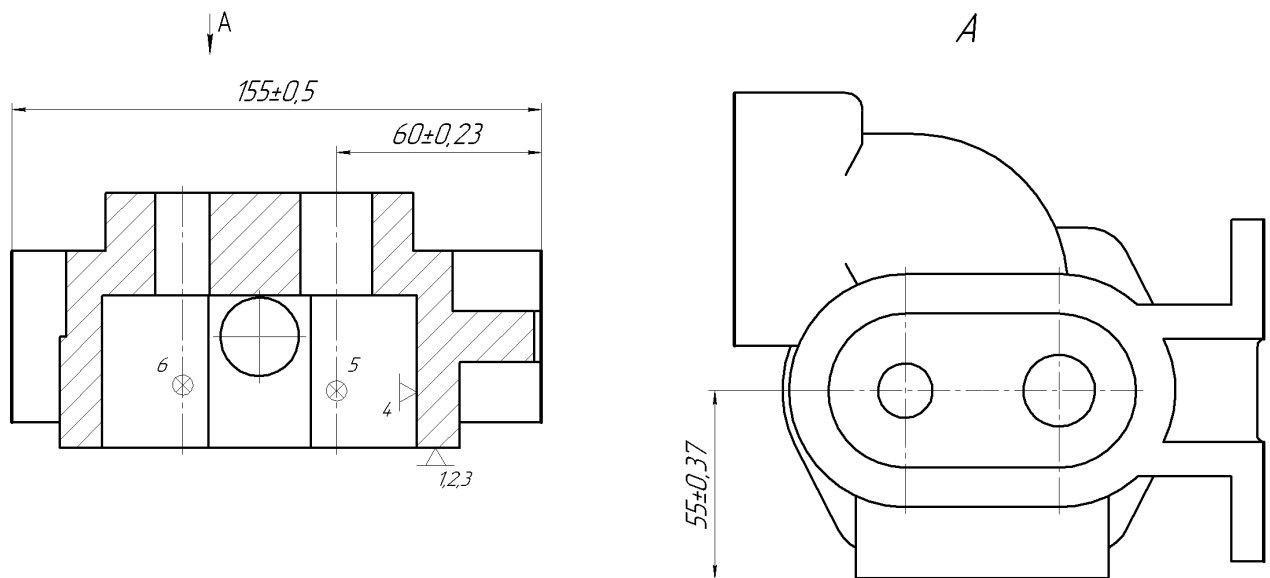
Схема базування заготовки на операції №005 «Горизонтально-фрезерна».
